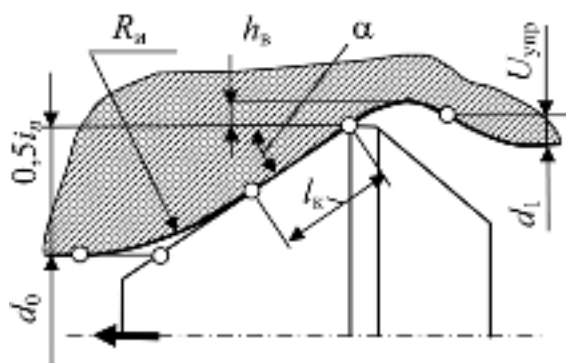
Схема очага деформации трубчатой заготовки при дорновании отверстия
